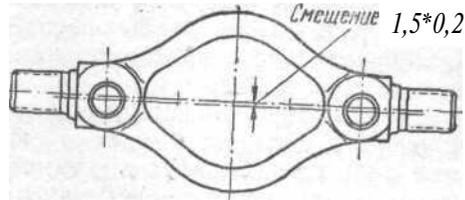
Ось верхнего рычага передней подвески автомобиля модели 407
